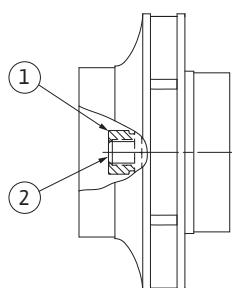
Posición correcta de la tuerca del rodete tras el montaje
